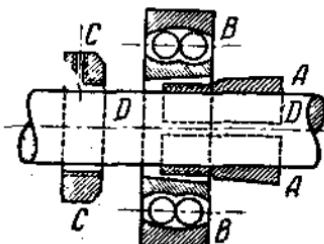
Крепление шарикоподшипника на валу с помощью конической втулки.
